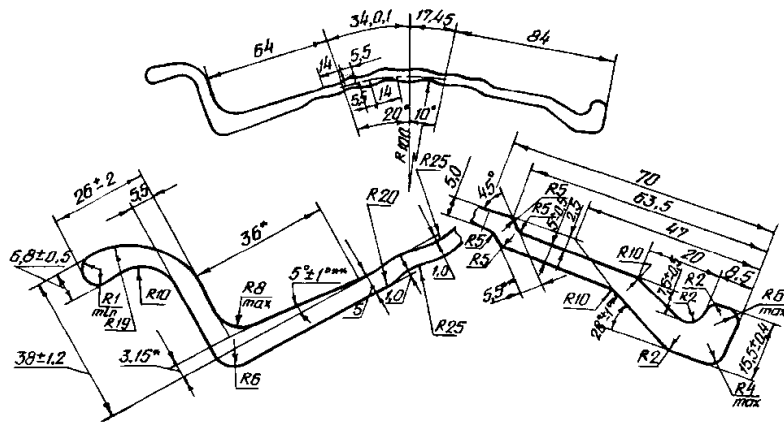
Рабочий чертеж профиля 7.0-20-03
